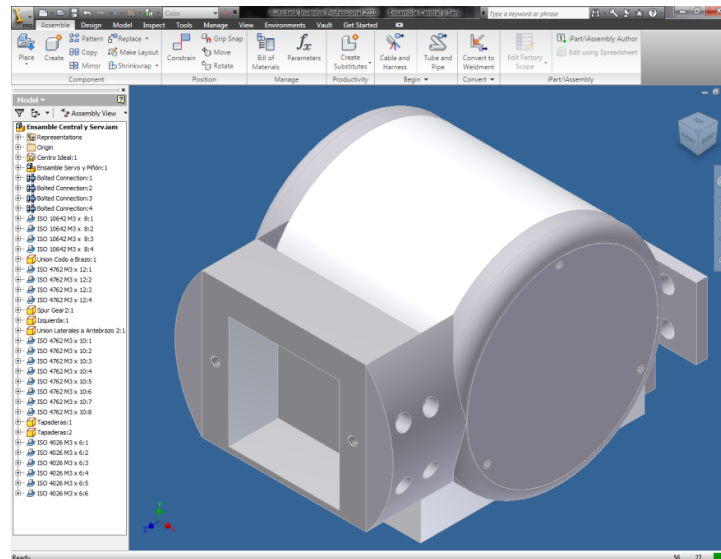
Modelo CAD del mecanismo de codo ensamblado sin las tapas
